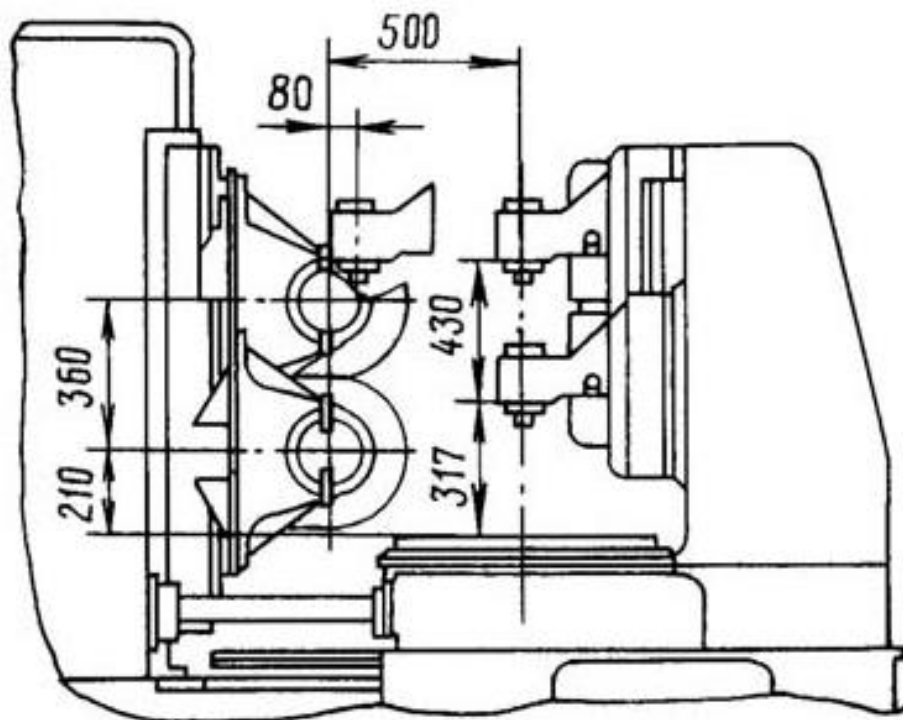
Габарити робочого простору верстата 5К32.
